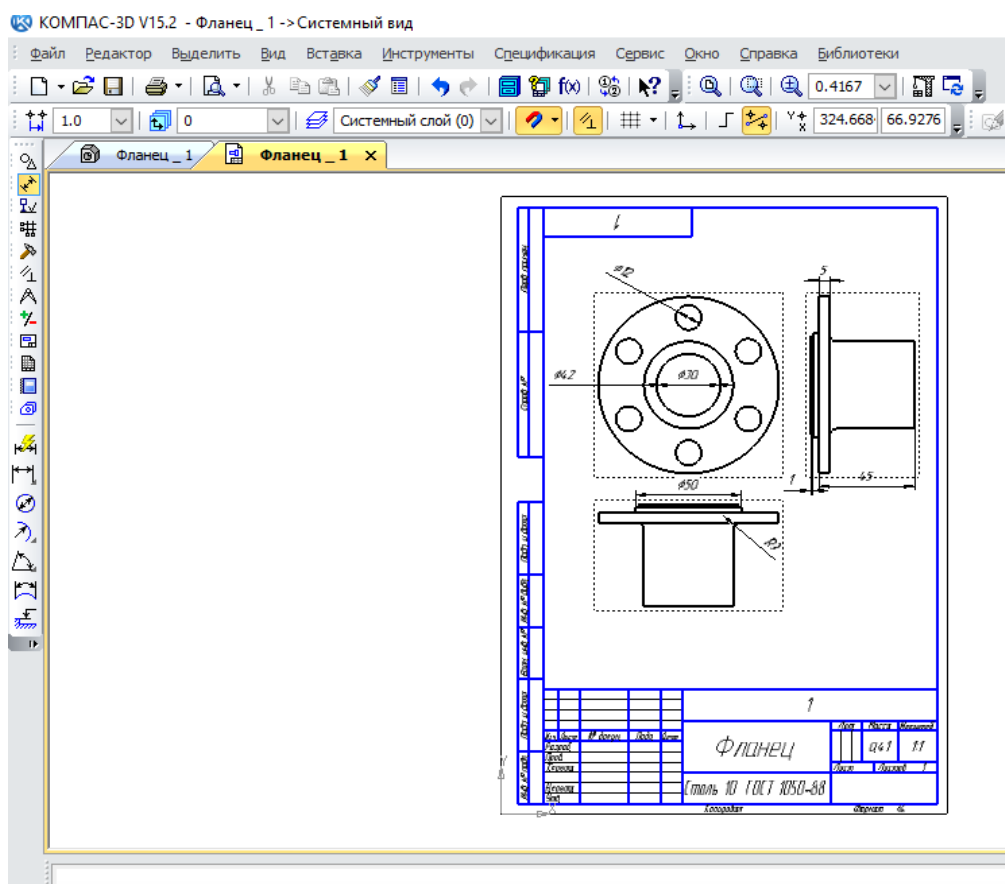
Ассоциативный чертеж отливки «Фланец»
